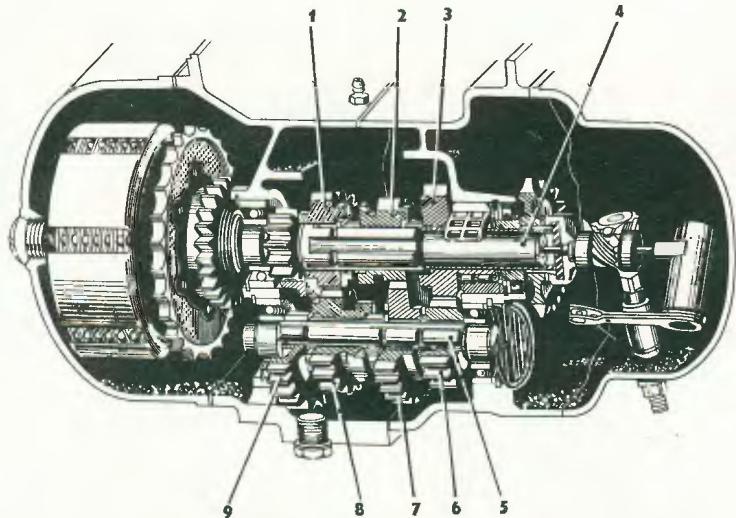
Коробка передач: 1 — неподвижная шестерня третьей передачи; 2 — подвижная шестерня второй передачи; 3 — вторичный вал; 4 — первичный вал; 5 — промежуточный вал; 6 — шестерня промежуточного вала; 7 — неподвижная шестерня второй передачи; 8 — подвижная шестерня третьей передачи; 9 — шестерня первой передачи.
